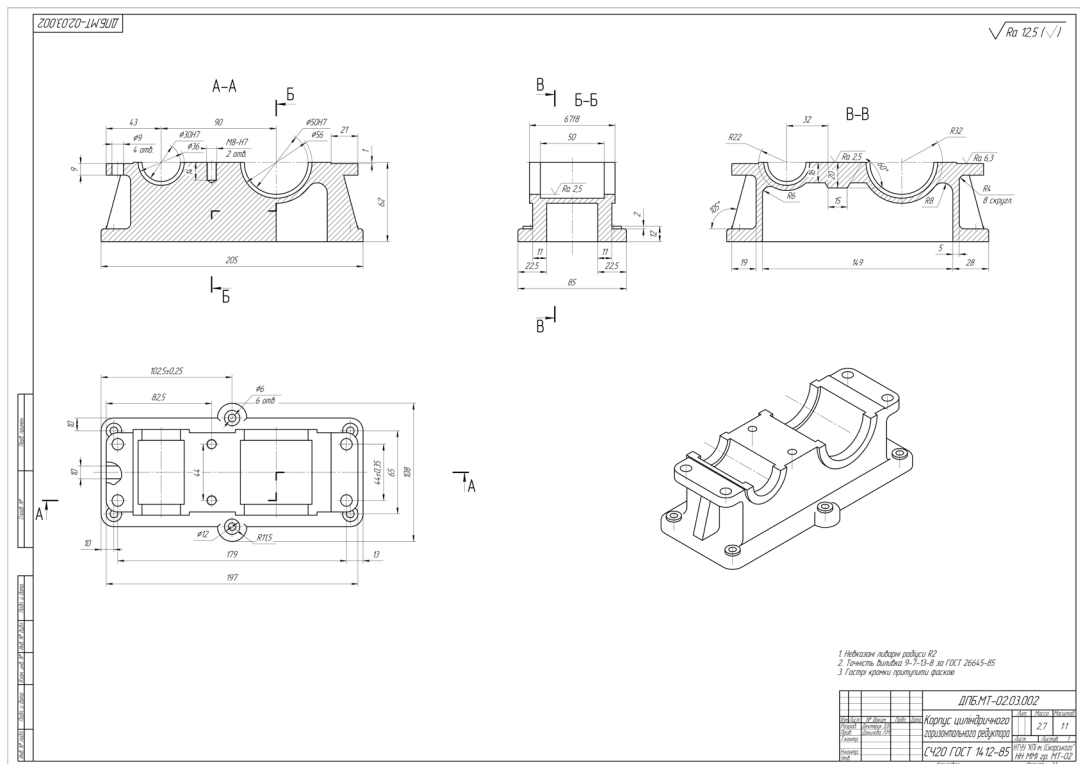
Креслення деталі «Корпус горизонтального редуктора»
